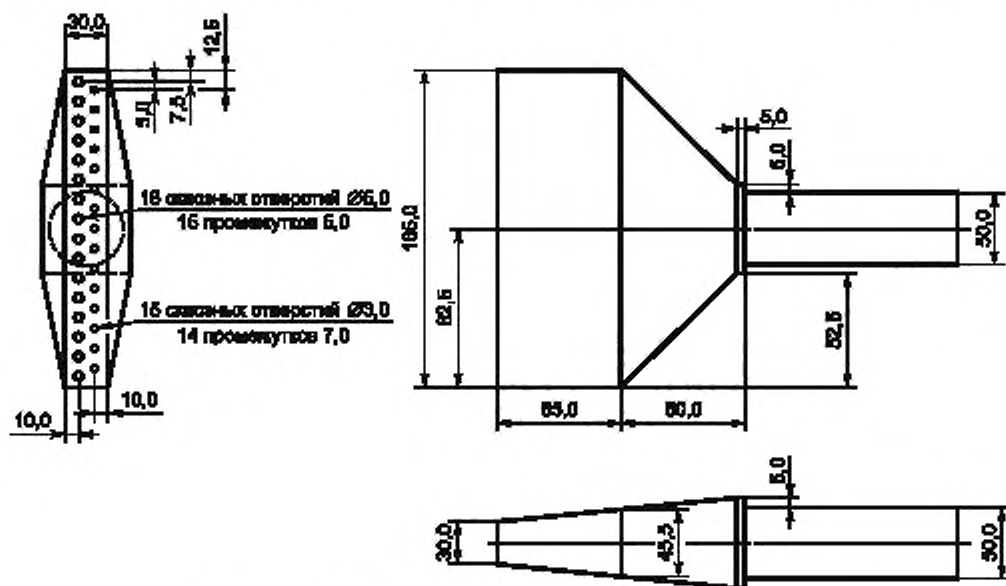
Насадка для подачи воды на дорожное покрытие
